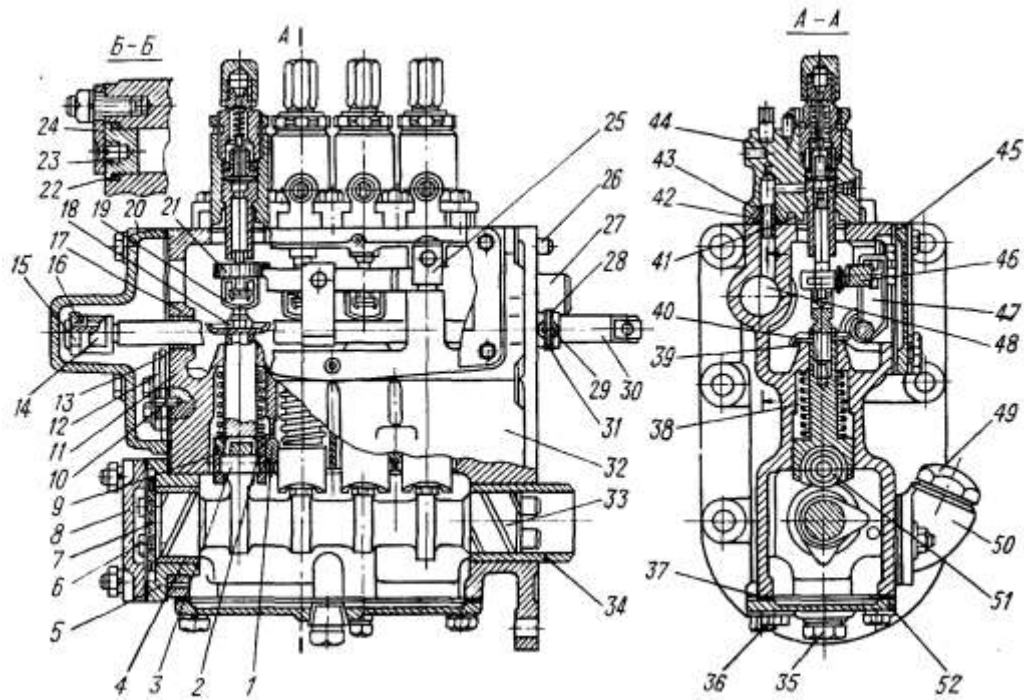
Топливный насос 14-67-сб2: 1 - направляющий палец; 2 - отверстие; 3 - ось толкателя; 4,17,34 - втулки; 5 - корпус заднего подшипника; 6 - болт; 7 - шайба; 8 - крышка подшипника; 9 - толкатель; 10 - установочный штифт; 11 -подкладка; 12 - накладка; 13 - пластинчатая пружина корректора; 14 - регулировочная муфта; 15,18 - контргайки; 16 - стопорный угольник; 19 - хвостовик толкателя; 20 - крышка корректора; 21 - зубчатый сектор; 22,42 - уплотнительные кольца; 23,27 - заглушки; 24 - прижим; 25 - направляющая пластина; 26,41 - установочные штифты; 28 - стопорное кольцо; 29 - палец; 30 - тяга; 31 - упорное кольцо; 32 - корпус насоса; 33 - кулачковый вал; 35 - пробка; 36 - штуцер; 37 - прокладка; 38 - пружина; 40 - тарелка; 43 - трубка; 44 - секция ТНВД; 45 - крышка бокового люка; 46 - рейка; 47 - поводок; 48 - канал; 49 - пробка; 50 - горловина; 51 - ролик толкателя; 52 - нижняя крышка люка.
